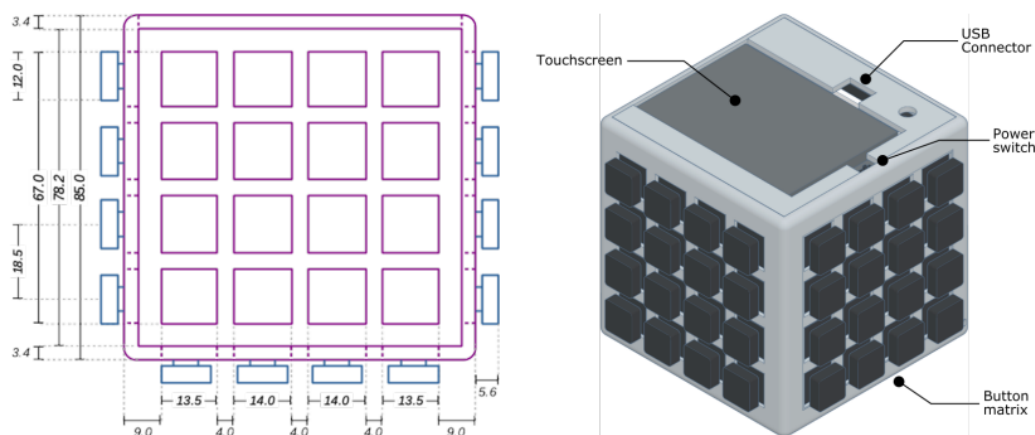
Размерный чертеж (слева) и 3D-модель (справа) прототипа KeyCube представленные «Upsidedown».
